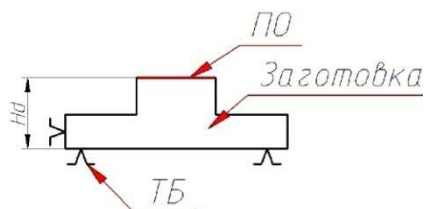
Схематичное представление эскиза заготовки на операции:
